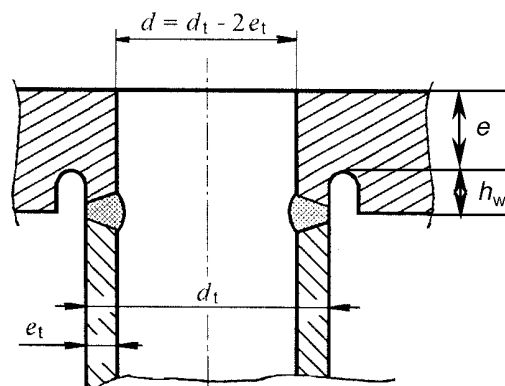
Tubo soldado a tope a la cara interior de la placa de tubos con ranura mecanizada
